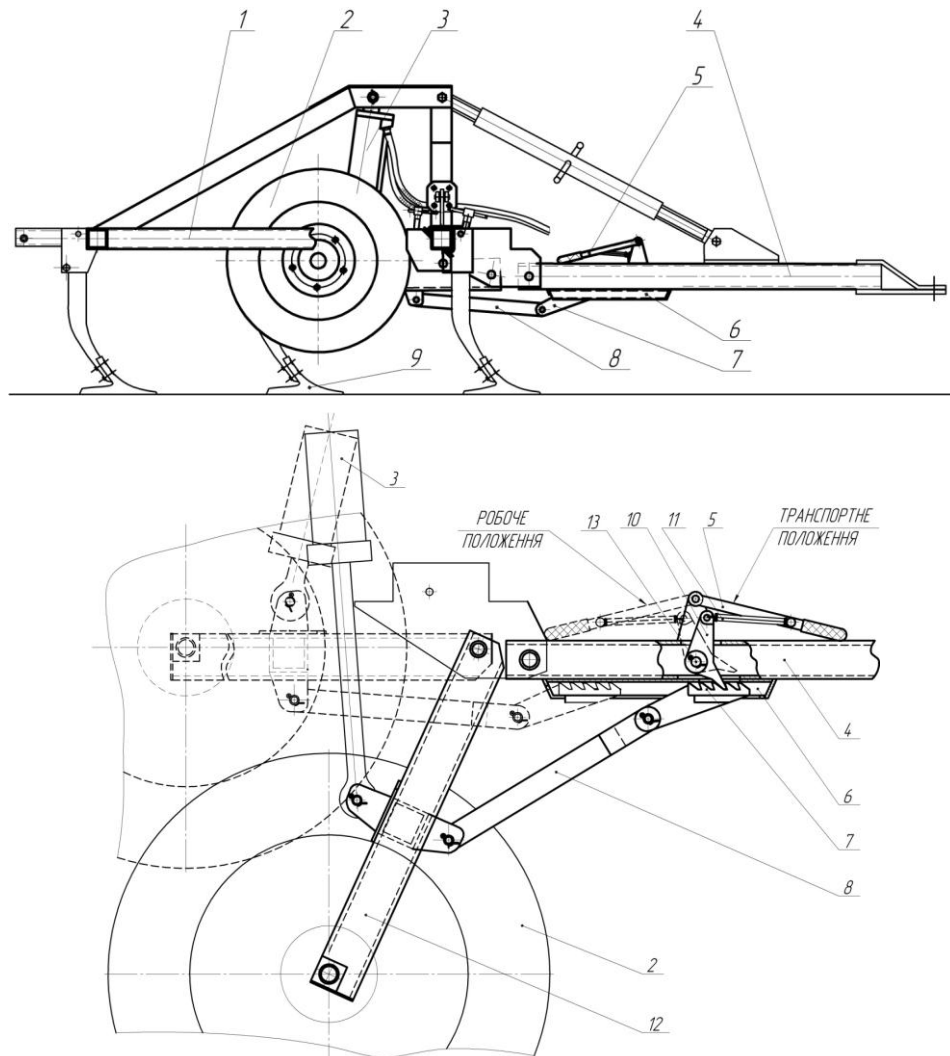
Загальний вигляд культиватора та механізму фіксації його транспортного положення
